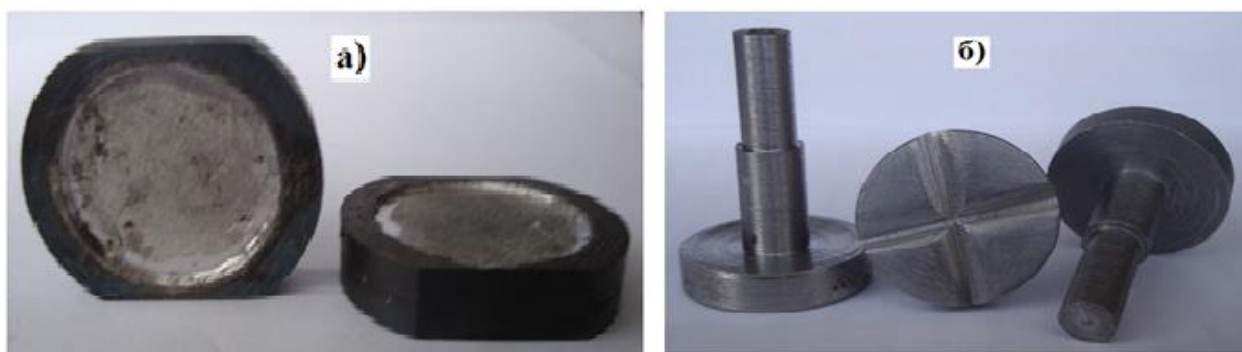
Комплект образцов для стенда на базе вертикально-сверлильного станка:
